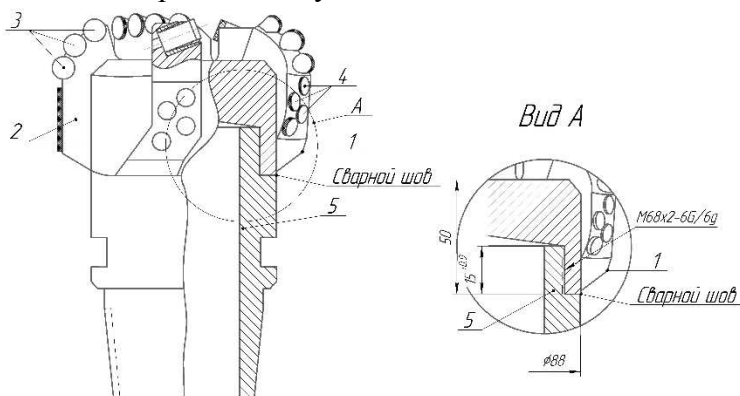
Алмазное долото: 1 – корпус долота, 2 – лопасти, 3 – резцы режуще-истирающего действия, 4 – резцы защитного действия, 5 – ниппель
